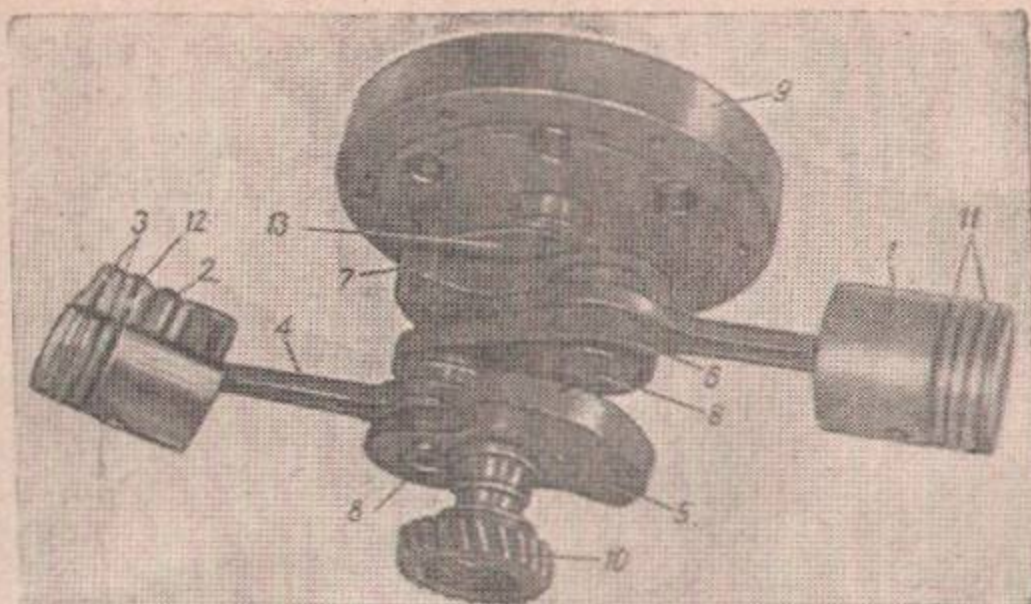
Кривошипный механизм с поршнями (в сборе):
